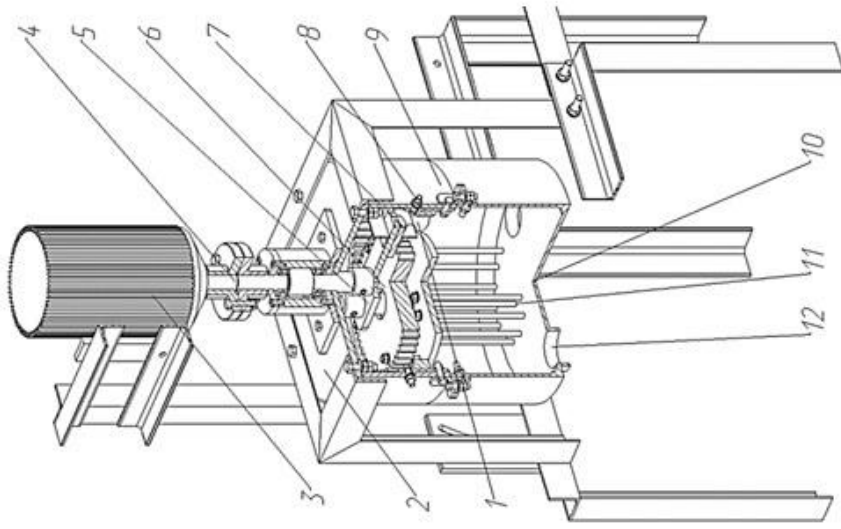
Змішувач силкових кормів: 1 - авантажувальний пристрій; 2 - кришка корпусу; 3-двигун; 4 - муфта; 5 - повідець; 6 - шестерня; 7 - противага; 8 - зубчастий вінець; 9 - корпус; 10 - ємність; 11 - мішалка; 12 - розвантажувальний пристрій
